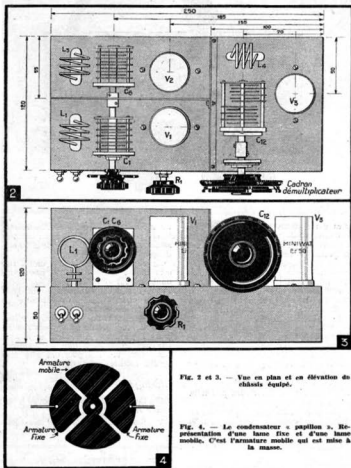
et 3. — Vue en plan et en élévation de châssis équipé.
